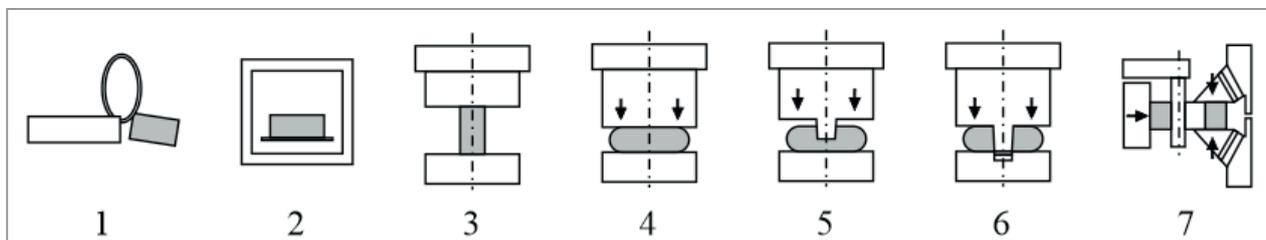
Технологический процесс изготовления кольцевых заготовок:
